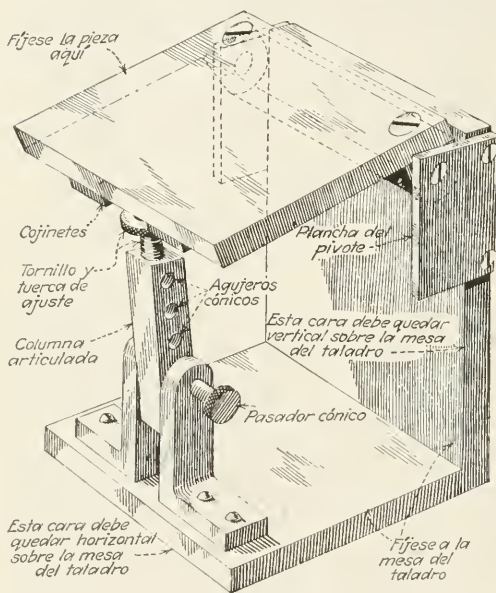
DISPOSICIÓN DEL ACCESORIO AJUSTABLE A CUALQUIER ÁNGULO
